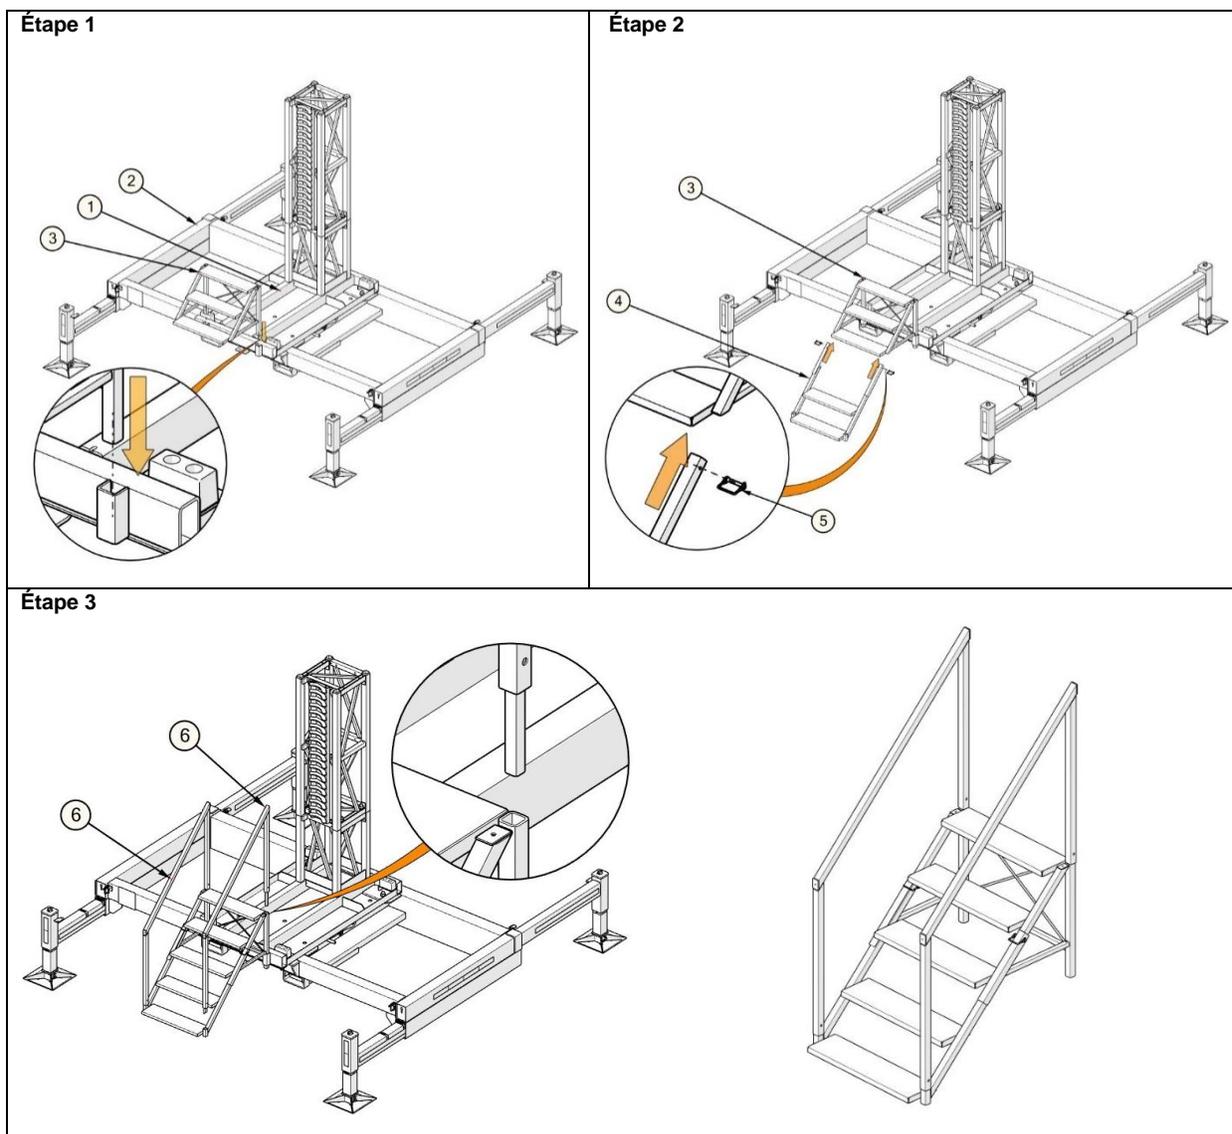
Installation de l'escalier 5 marches sur base autoportante
